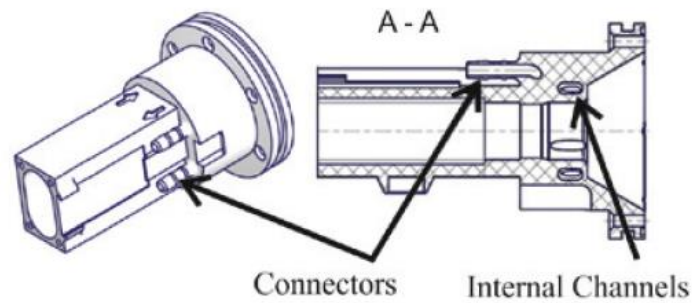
Vista laterale e prospettica del componente riprogettato
